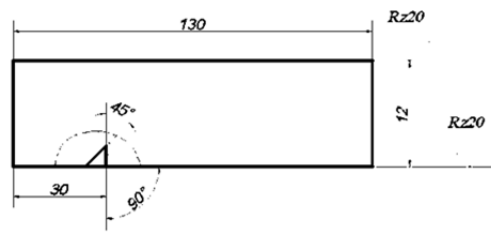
Эскиз настроечного стандартного образца предприятия с зарубкой
